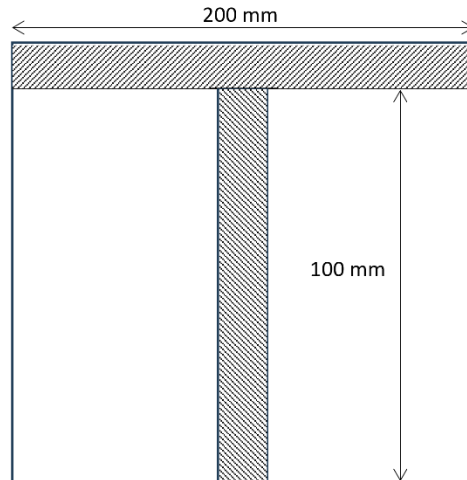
Vista frontal, con dimensiones, de ménsula.
